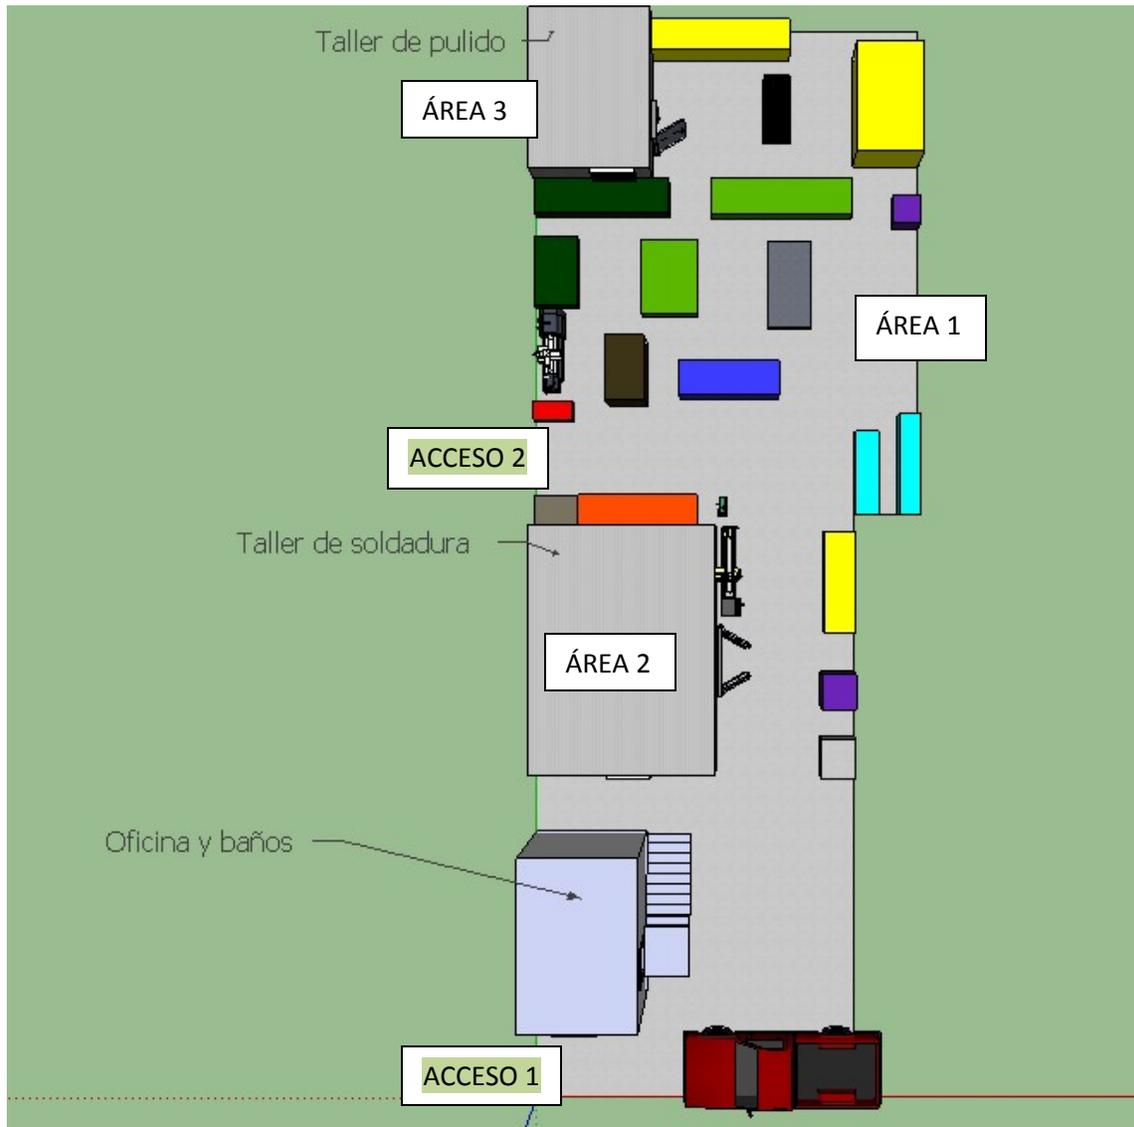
Vista planta, distribución de áreas, maquinaria y equipo
